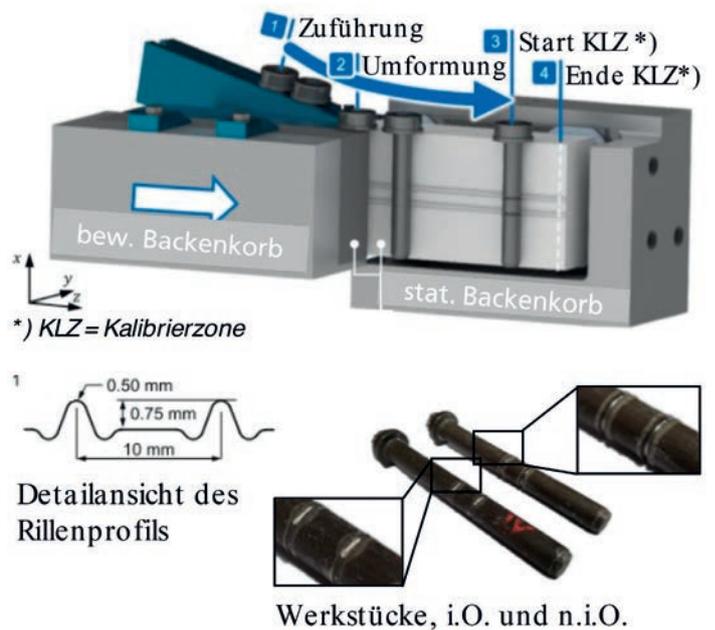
Versuchswerkzeug, Detailansicht des Rillenprofils sowie i.O.- und n.i.O.-Teil
